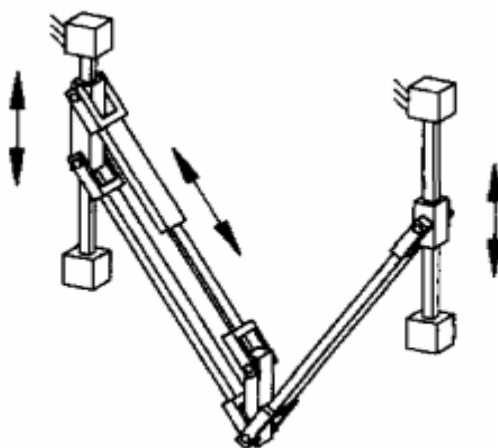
Планарный последовательно-параллельный механизм с тремя степенями свободы [3]
